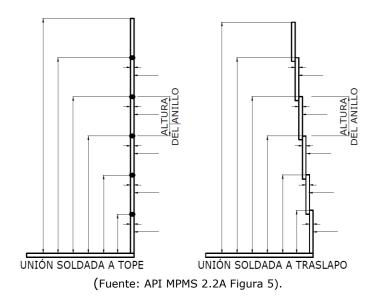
Posiciones para Medición de Circunferencias en Tanques Soldados.
